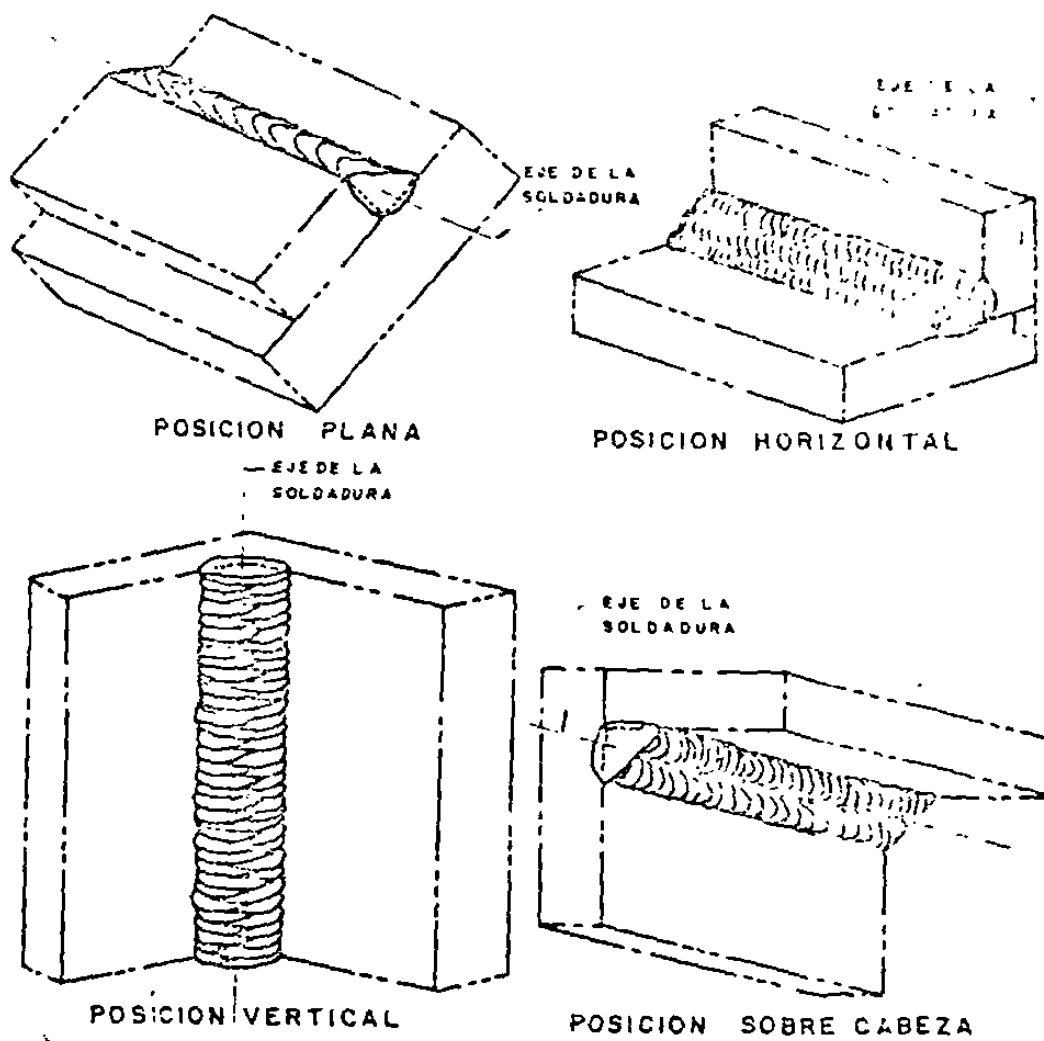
POSICION AL SOLDAR PARA SOLDADURA DE FILETE
